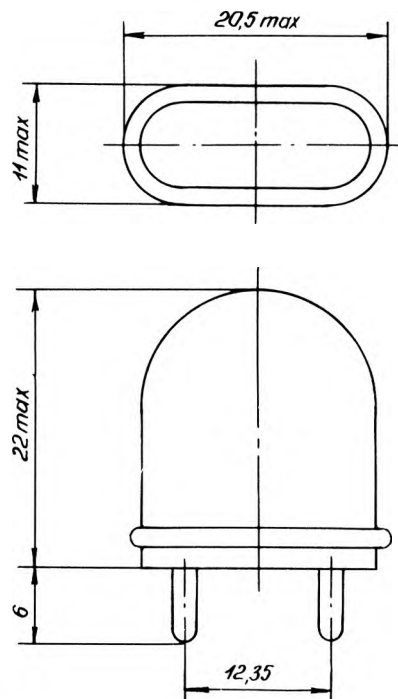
Габаритные, установочные и присоединительные размеры резонатора (корпус КБ)
